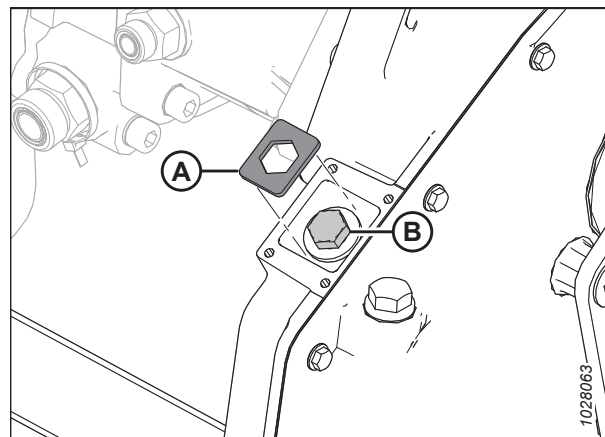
Hauptgetriebe mit Kettenspanner
